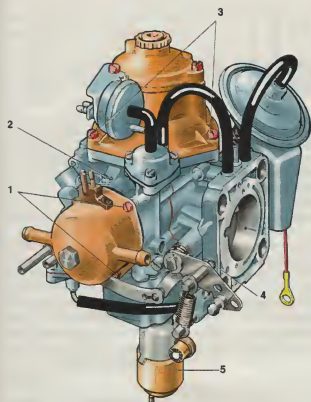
Общий вид карбюратора "Стромберг" (с 1980 года): 1 — винты крепления крышки; 2 — полуавтоматическое устройство пуска и прогрева; 3 — винты крепления верхней крышки, открывающей доступ к диафрагме; 4 — регулировочный винт оборотов холостого хода; 5 — клапан подачи топлива.
